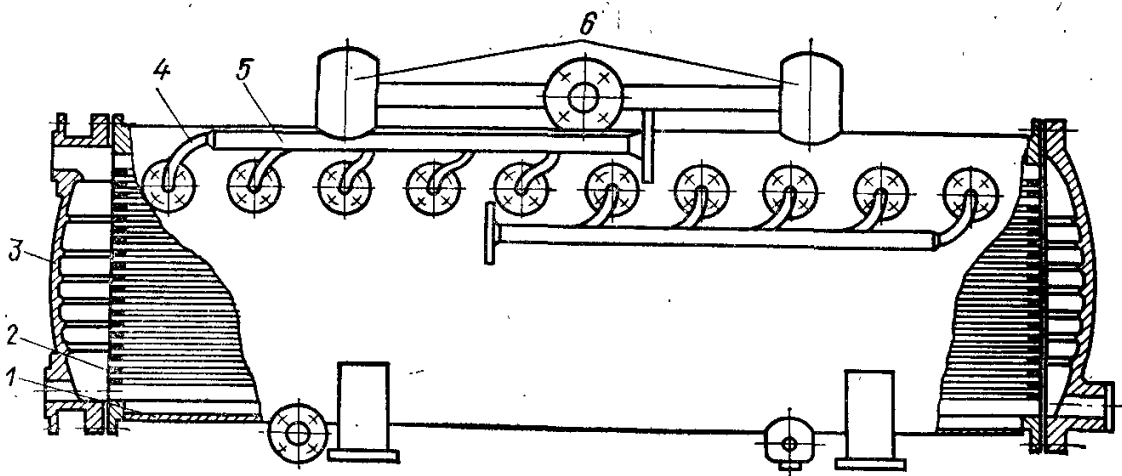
Зрошувальний кожухотрубчастий випарник
